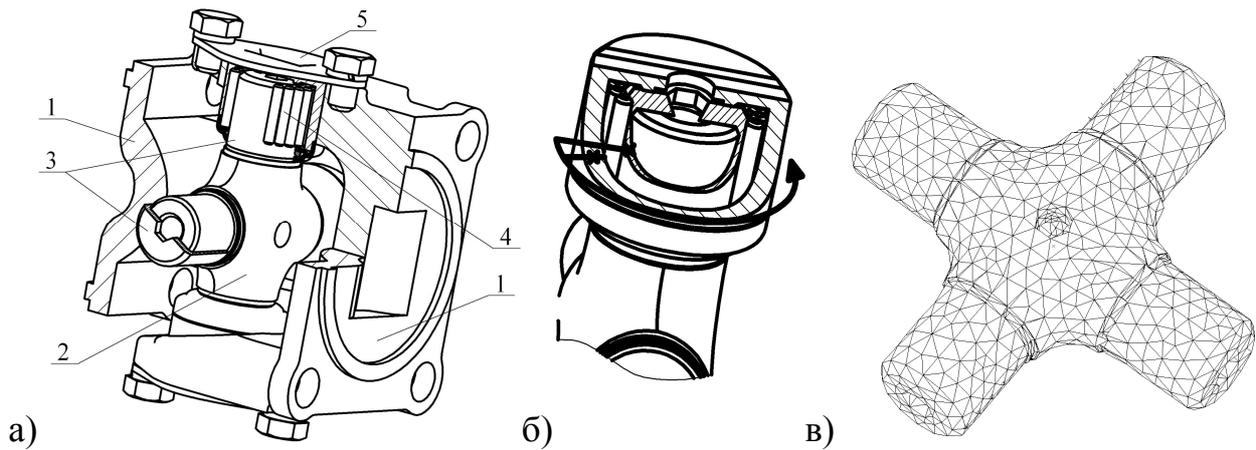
Карданный шарнир (RU 2232309): а) схема карданного шарнира; б) поворот игольчатого подшипника и втулки; в) конечно-элементная модель крестовины; 1 – вилка; 2 – крестовина; 3 – втулка; 4 - игольчатый подшипник 5 – крышка
